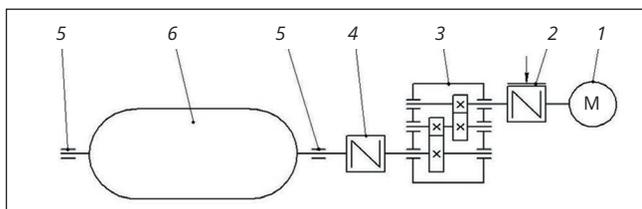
Кинематическая схема привода вращения автоклава до модернизации: 1 – электродвигатель; 2 – муфта с тормозом; 3 – редуктор; 4 – муфта; 5 – подшипниковые узлы; 6 – автоклав
